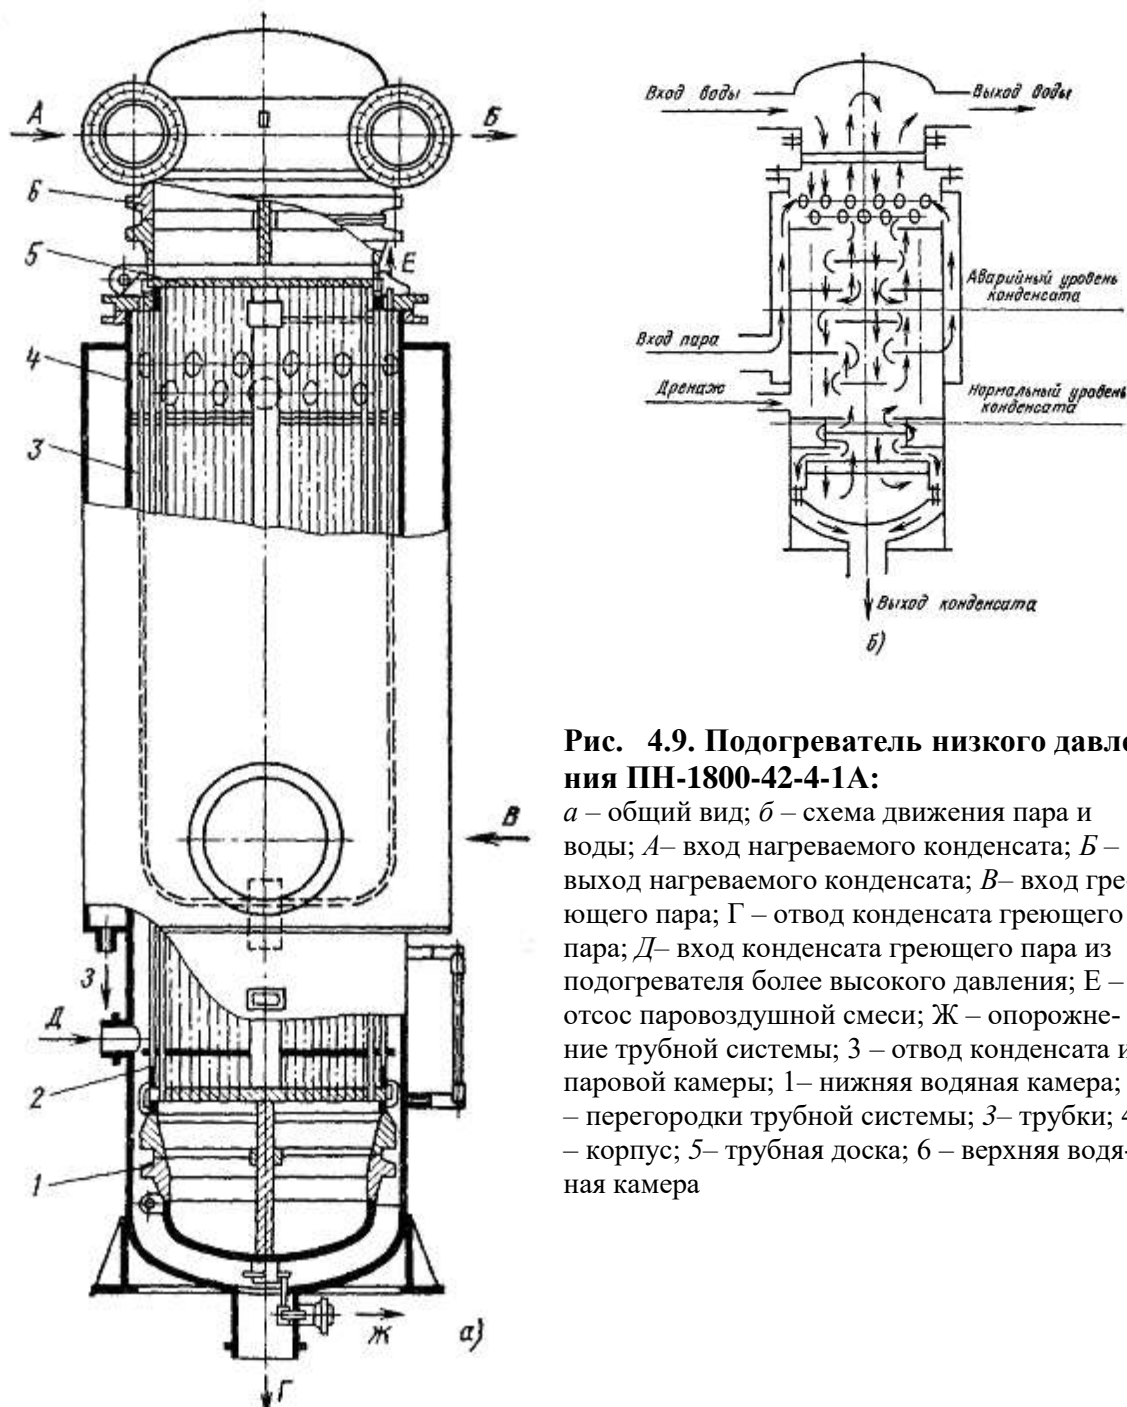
Подогреватель низкого давления ПН-1800-42-4-1А:
